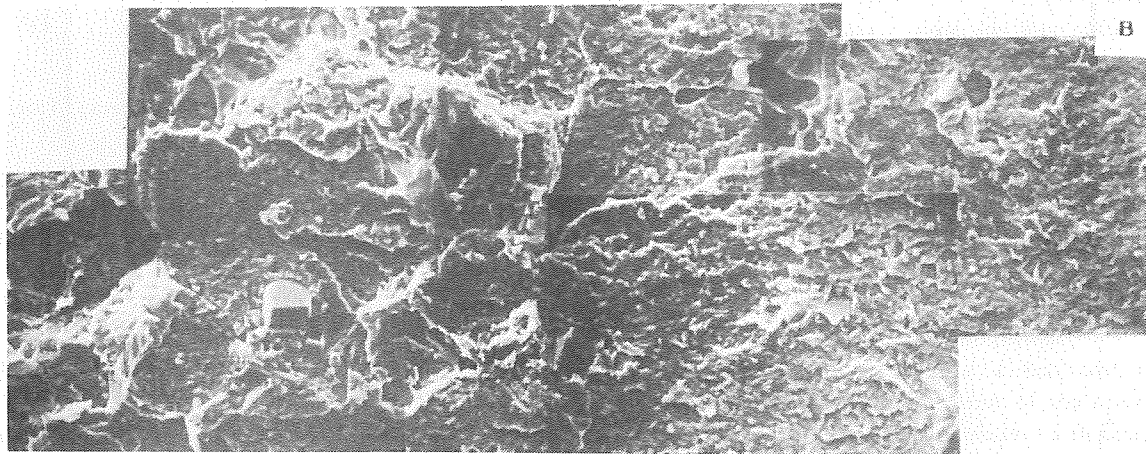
a) Fractura de probeta sinterizada en gas y revenida a 620°C
